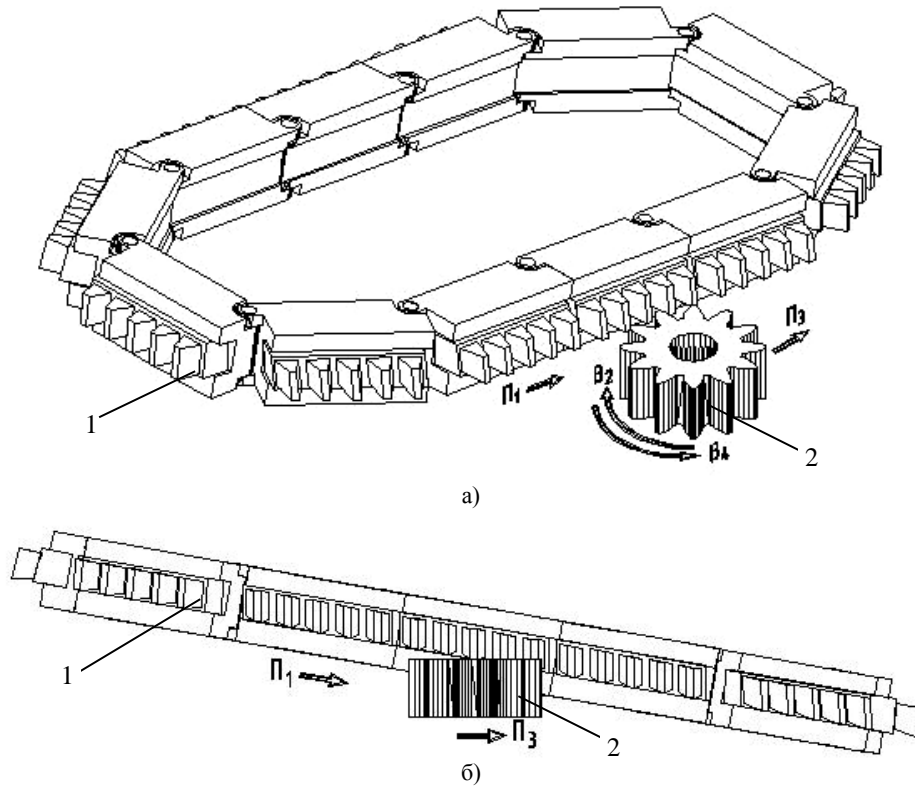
Схема зуботочения цепным инструментом реечного типа при тангенциальной подаче заготовки
